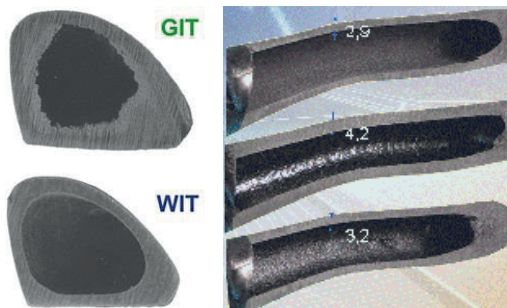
Prinzip der WIT Technik – langer Spritzguss
